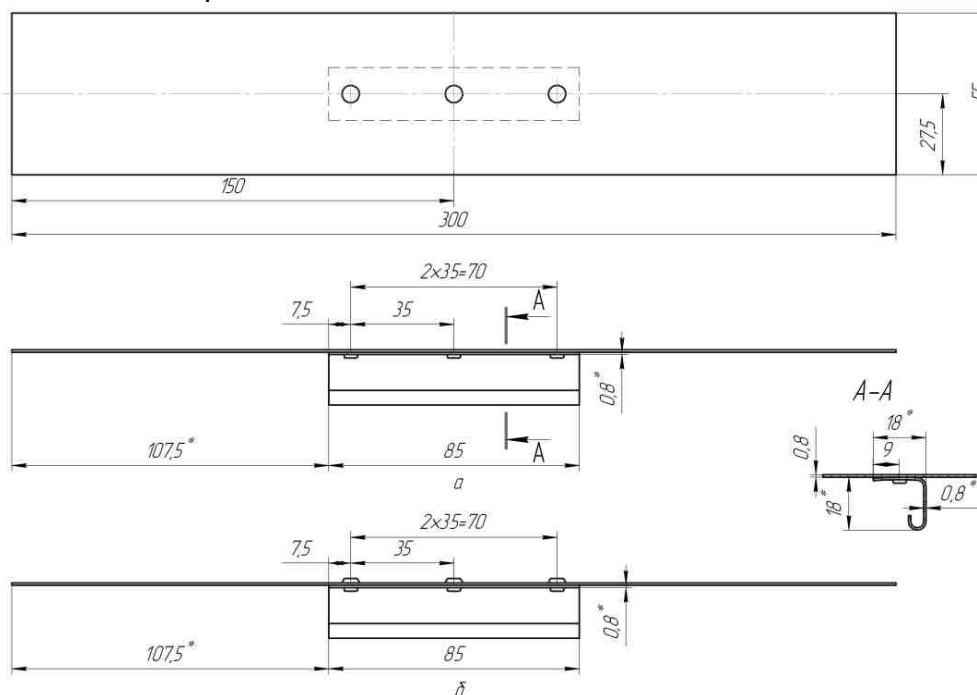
Фрагмент чертежа соединения с одной накладкой и шагом заклепок 35 мм: а – с потайными заклепками; б – с заклепками с плоско-скругленной головкой
